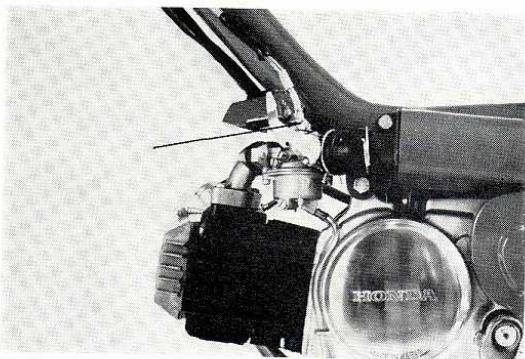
DEMONTAGE DU CABLE DES GAZ.
